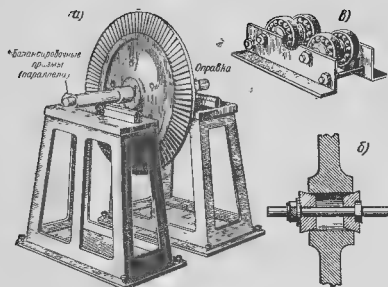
Станок для статической балансировки дисков. а — балансировка на призмах; б — установка диска на конических втулках; в — спаренные шарикоподшипники, замещающие призмы.
